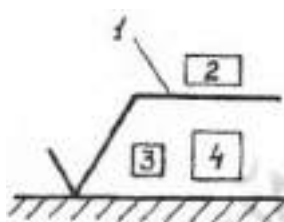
Обозначения шероховатости поверхностей.
